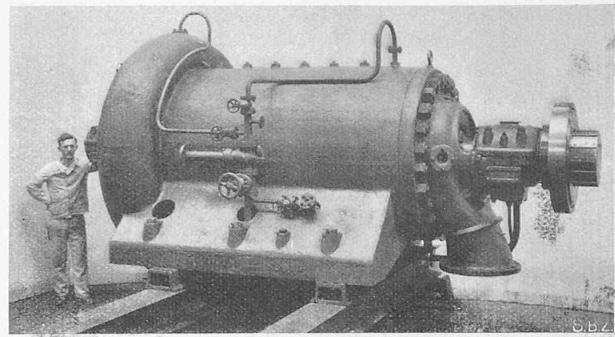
Ansicht einer der Hochdruck-Pumpen von Escher Wyss & Cie.
